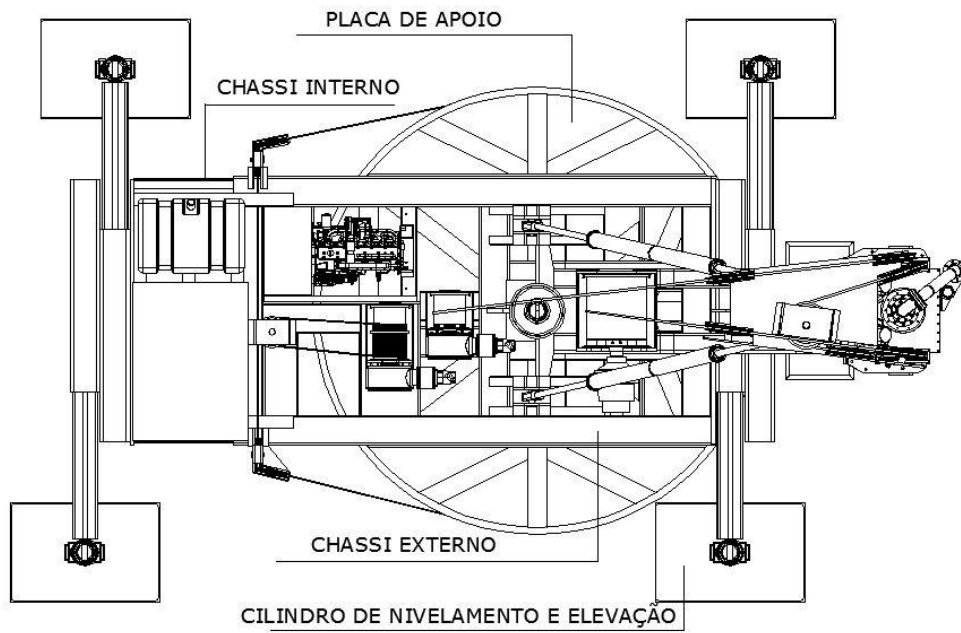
Desenho de conjunto da perfuratriz. Vista em planta.
